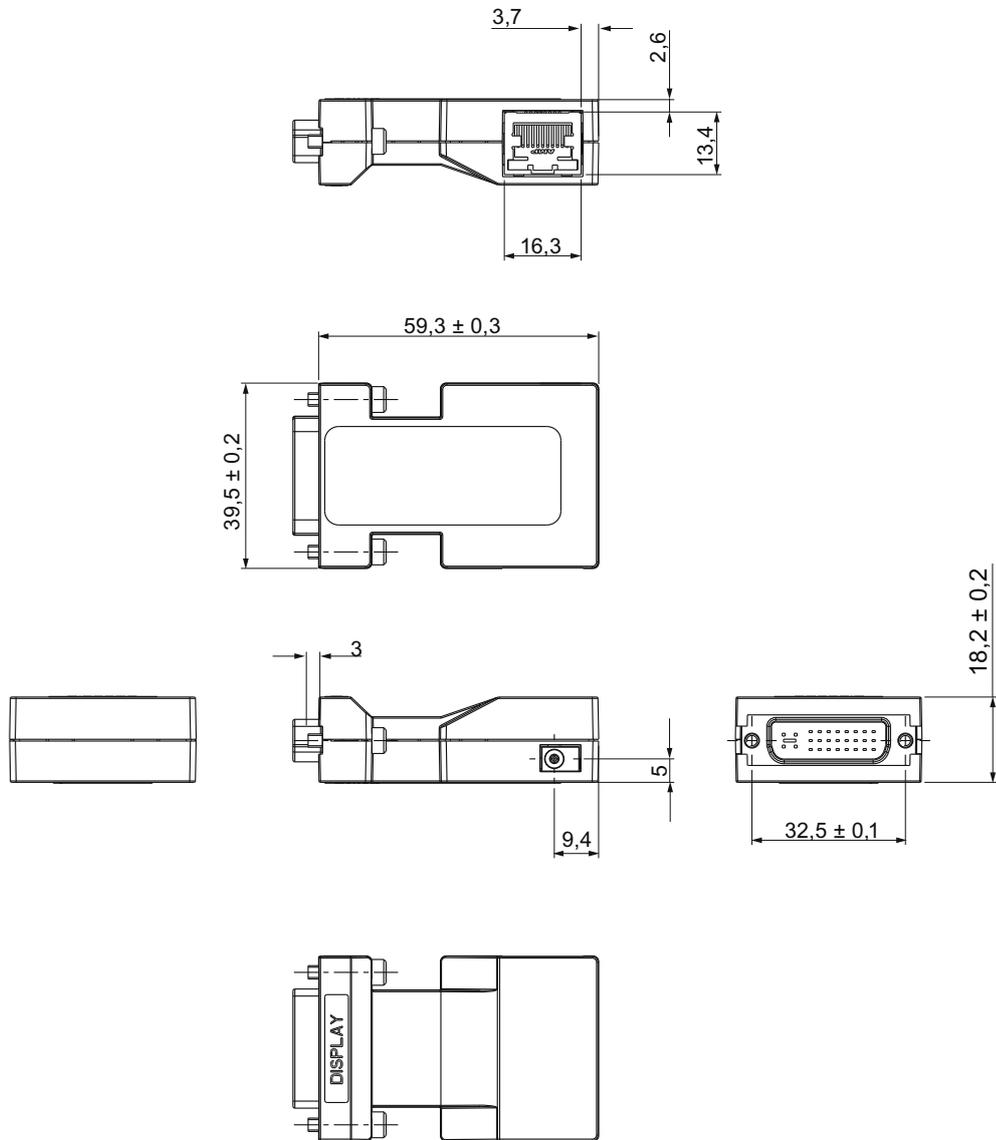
Ansichten des Empfängermoduls, Kabelanschluss seitlich
